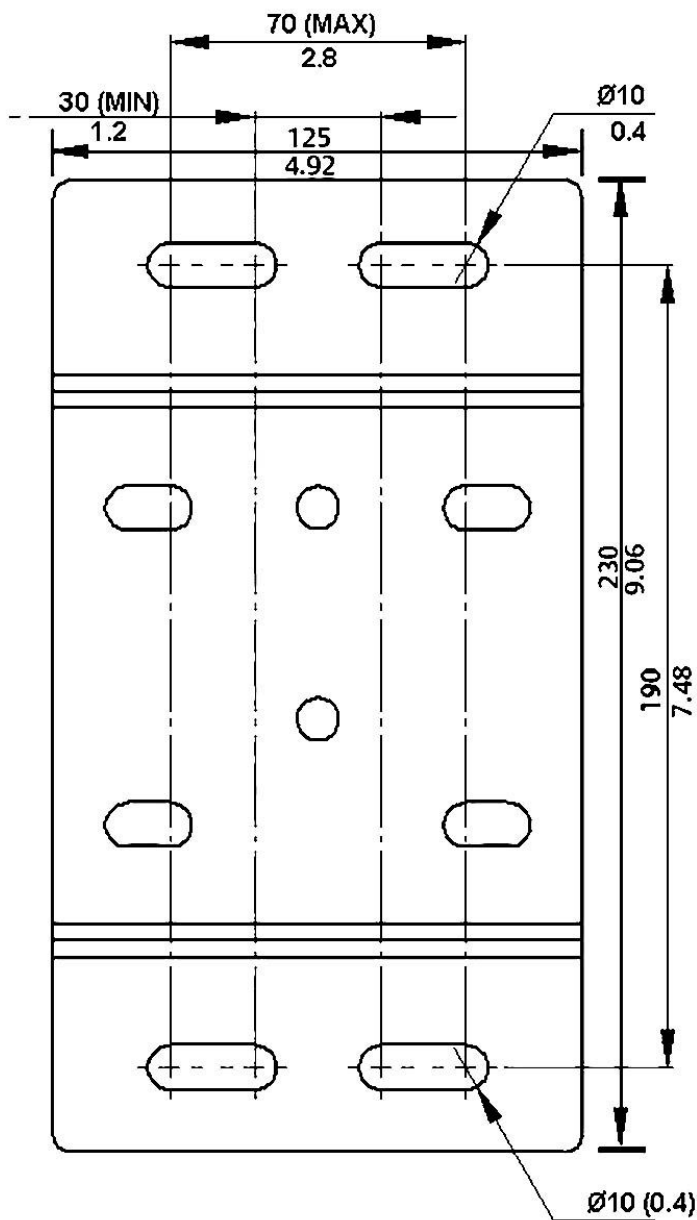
mostra a posição dos slots de montagem no suporte de montagem de parede fornecido com o GDU-Incus padrão. Perfure pares de \varnothing 0,4 pol. (10 mm) orifícios na superfície de montagem entre 1,2 pol. (30 mm) e 2,8 pol. (70 mm) de distância, com uma distância vertical de 7,48 pol. (190 mm) entre os dois pares de orifícios.
